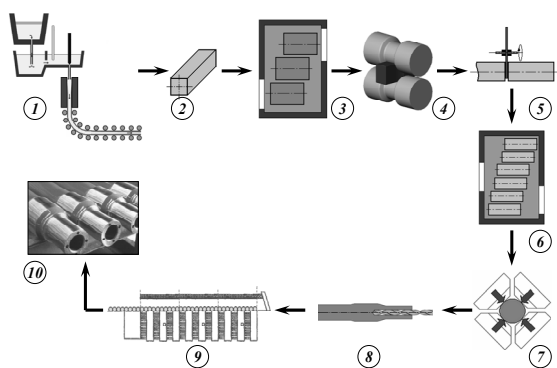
Вариант технологии изготовления полрой оси из сплошной непрерывнолитой заготовки квадратного сечения (продольная прокатка - ковка)
